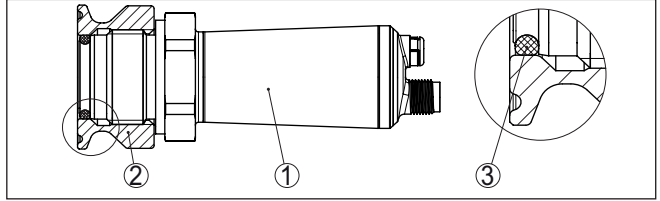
O-Ring-Dichtung G1 VEGABAR
